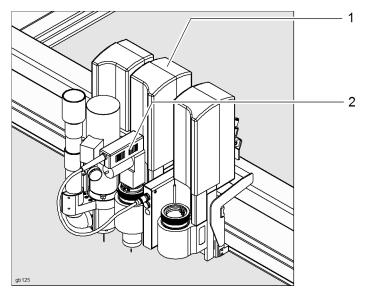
Punto d'innesto, assegnazione utensile ad es. modulo 2, utensile 1
